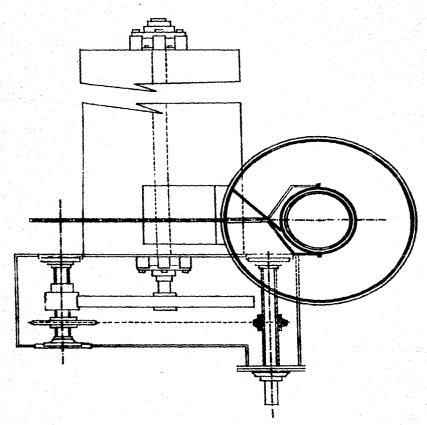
VISTA DE PLANTA DEL ALIMENTADOR DE PLATO Y PRE-HIDRATADOR
